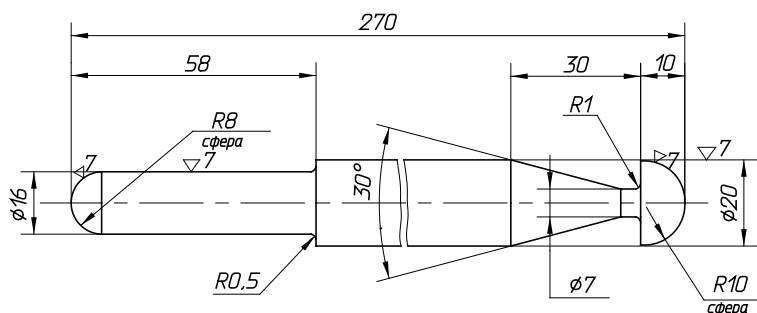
Оправка направляющая для установки крышек коренных подшипников.
